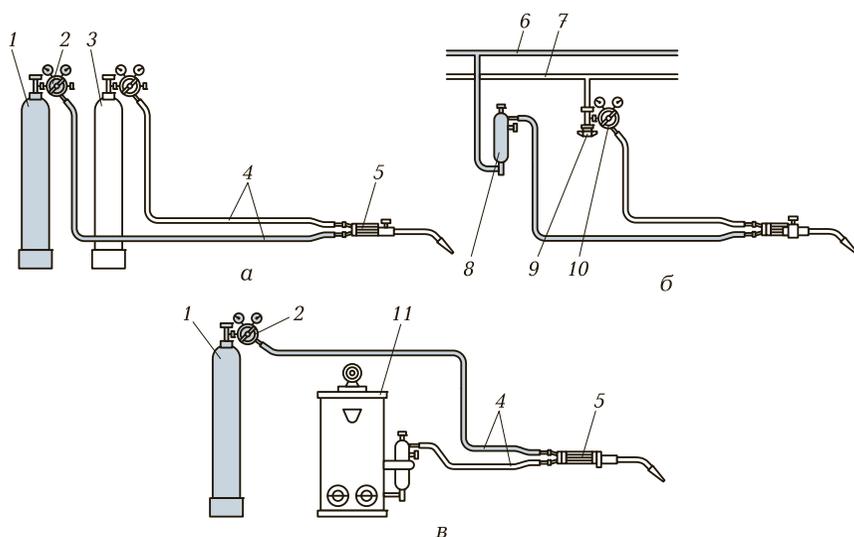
Схемы газопитания сварочного поста:
